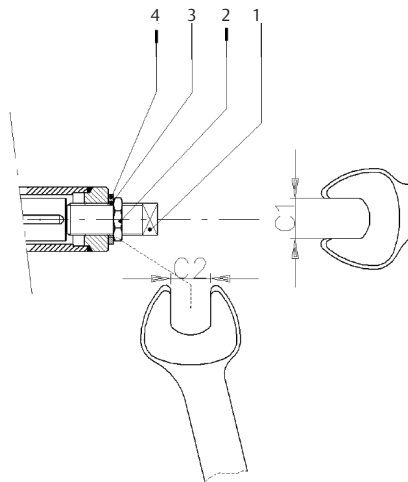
Mechanischer Anschlag am Endflansch der Handnotbetätigung
